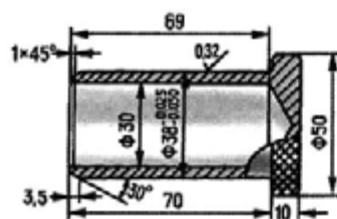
Пробка-заглушка в удлинителе коробки передач
